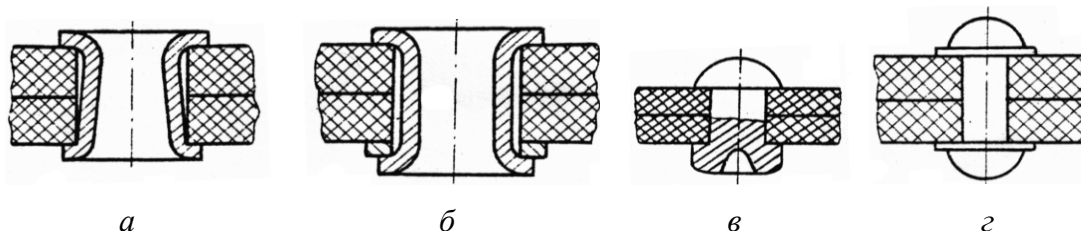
Соединение пластмассовых деталей с помощью заклепок
